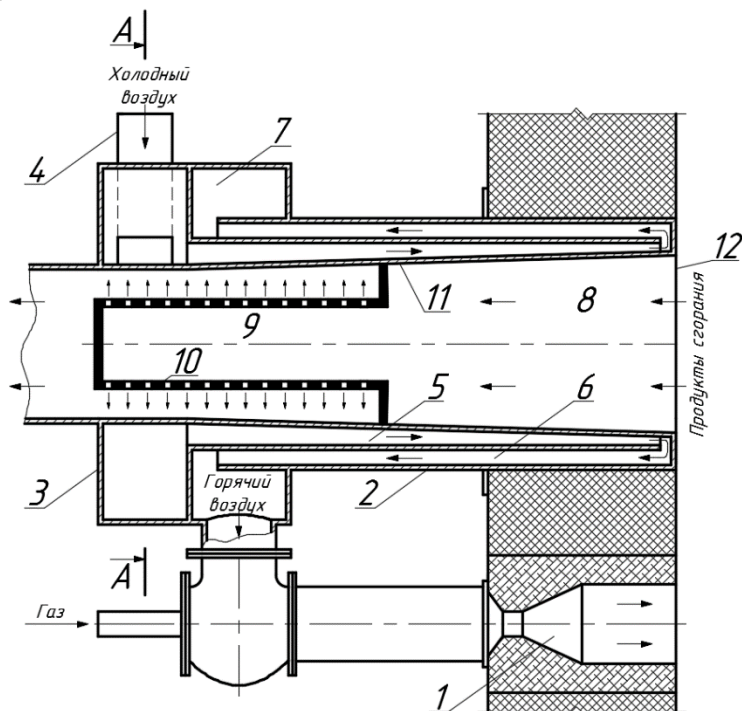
Продольный разрез рекуперативно-горелочного блока
